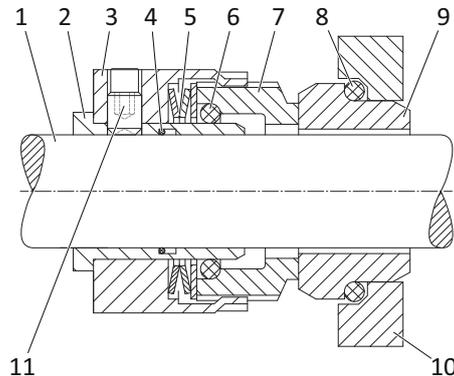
Aufbau entlastete Gleitringdichtung mit Sinusfeder
